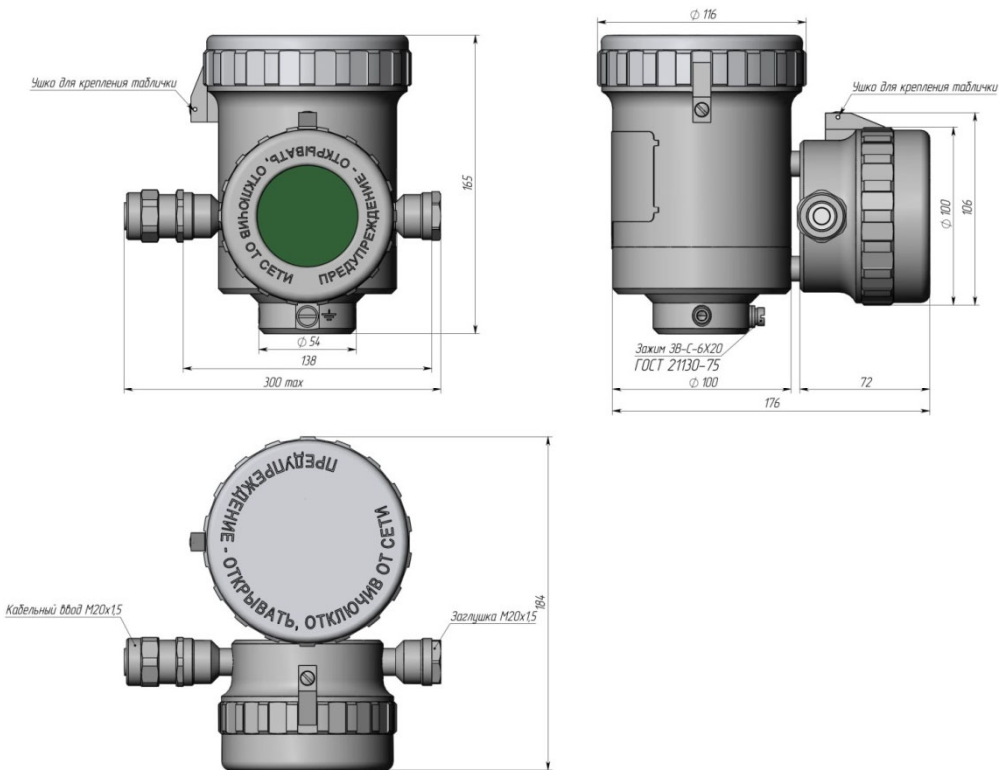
Габаритные и установочные размеры корпуса из нержавеющей стали блока электронного преобразователя. Класс безопасности ЗН. IP67. Дисплей сбоку
